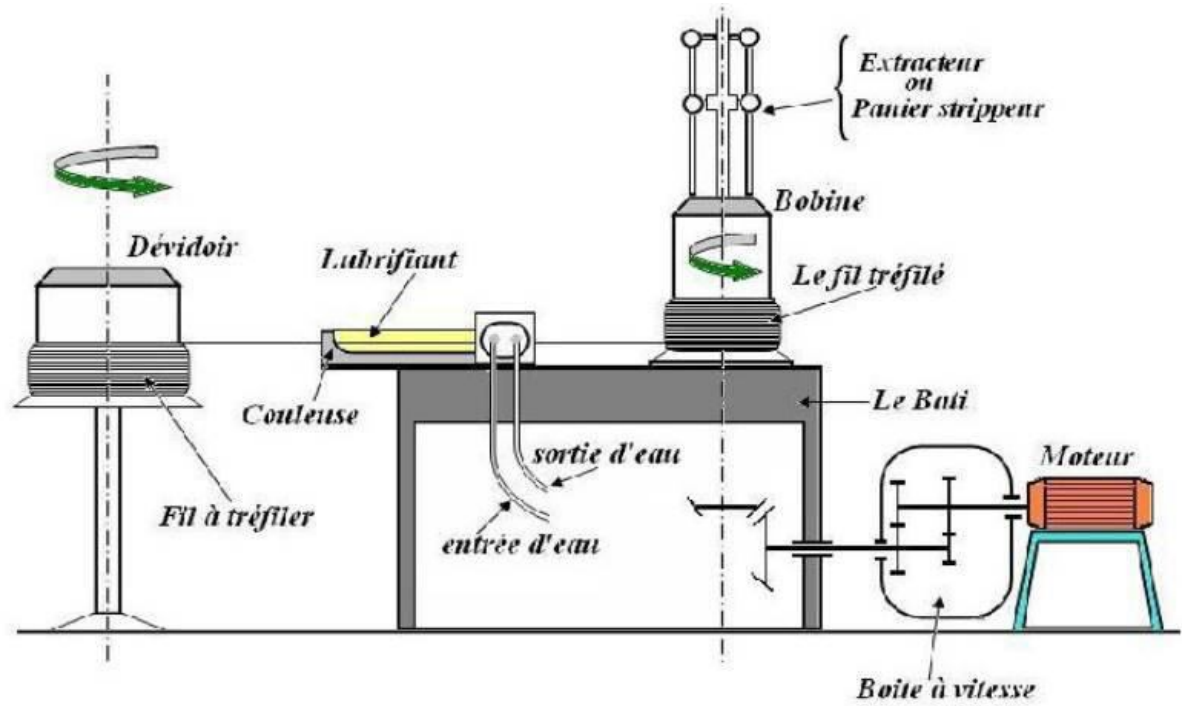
Schéma d'une machine à tréfilé multi-passe [29].
